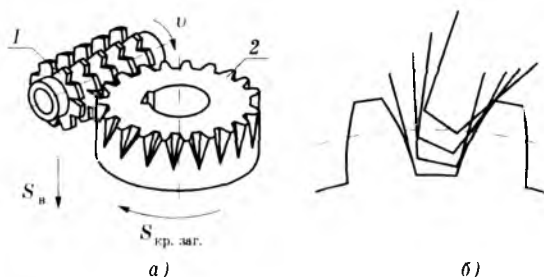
Схемы фрезерования зубьев зубчатых колёс методом обкатки (огибания):
